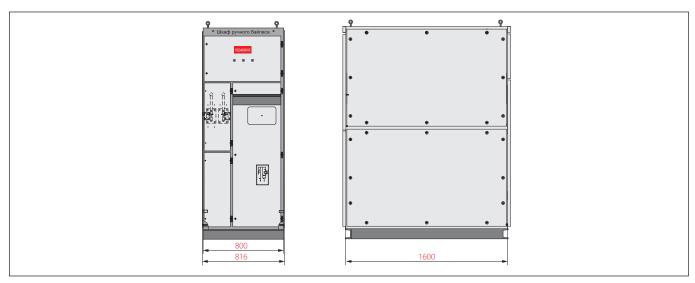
Корпус шкафа ручного байпаса типоразмера МВ02
